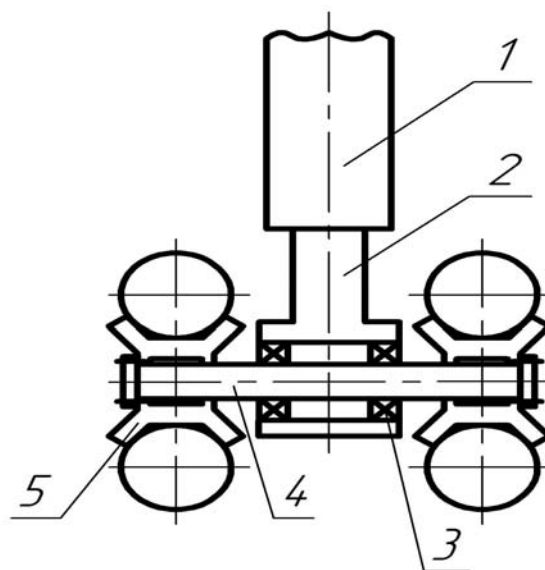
Схема блокировки колес опоры шасси самолета
